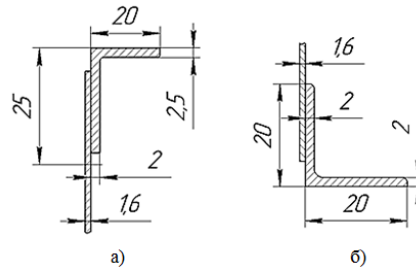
Поперечний переріз силових елементів – а) – верхній пояс; б) – нижній
